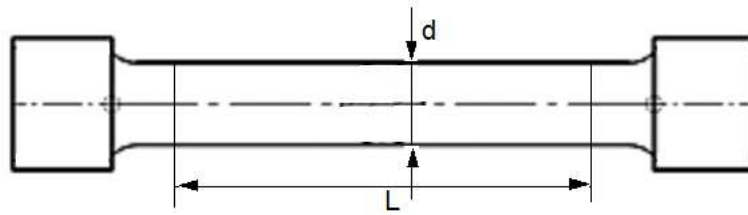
Probenstab für den Zugversuch gemäß EN 1563
